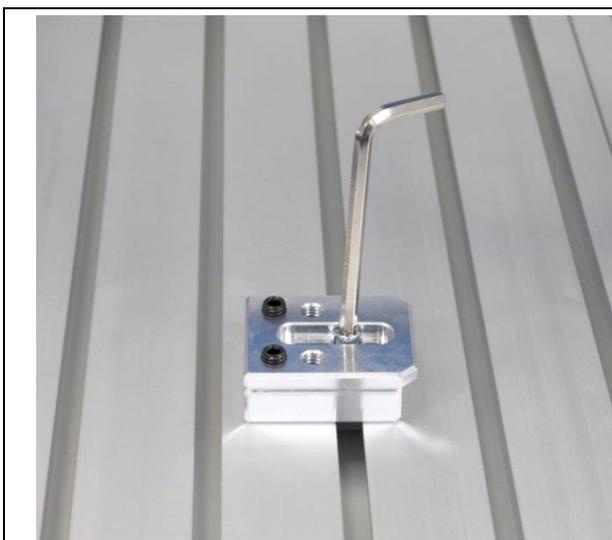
Spannpratze mittels Zylinderschraube auf T-Nutenplatte befestigen
